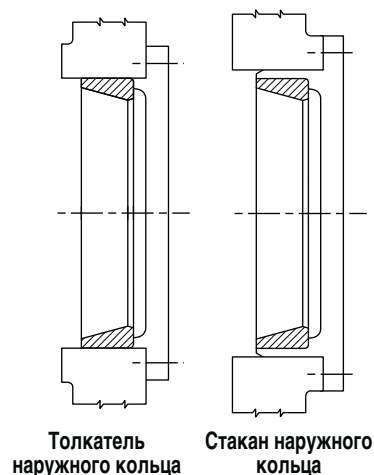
Приспособления для регулировки подшипников (схема монтажа «О»).
